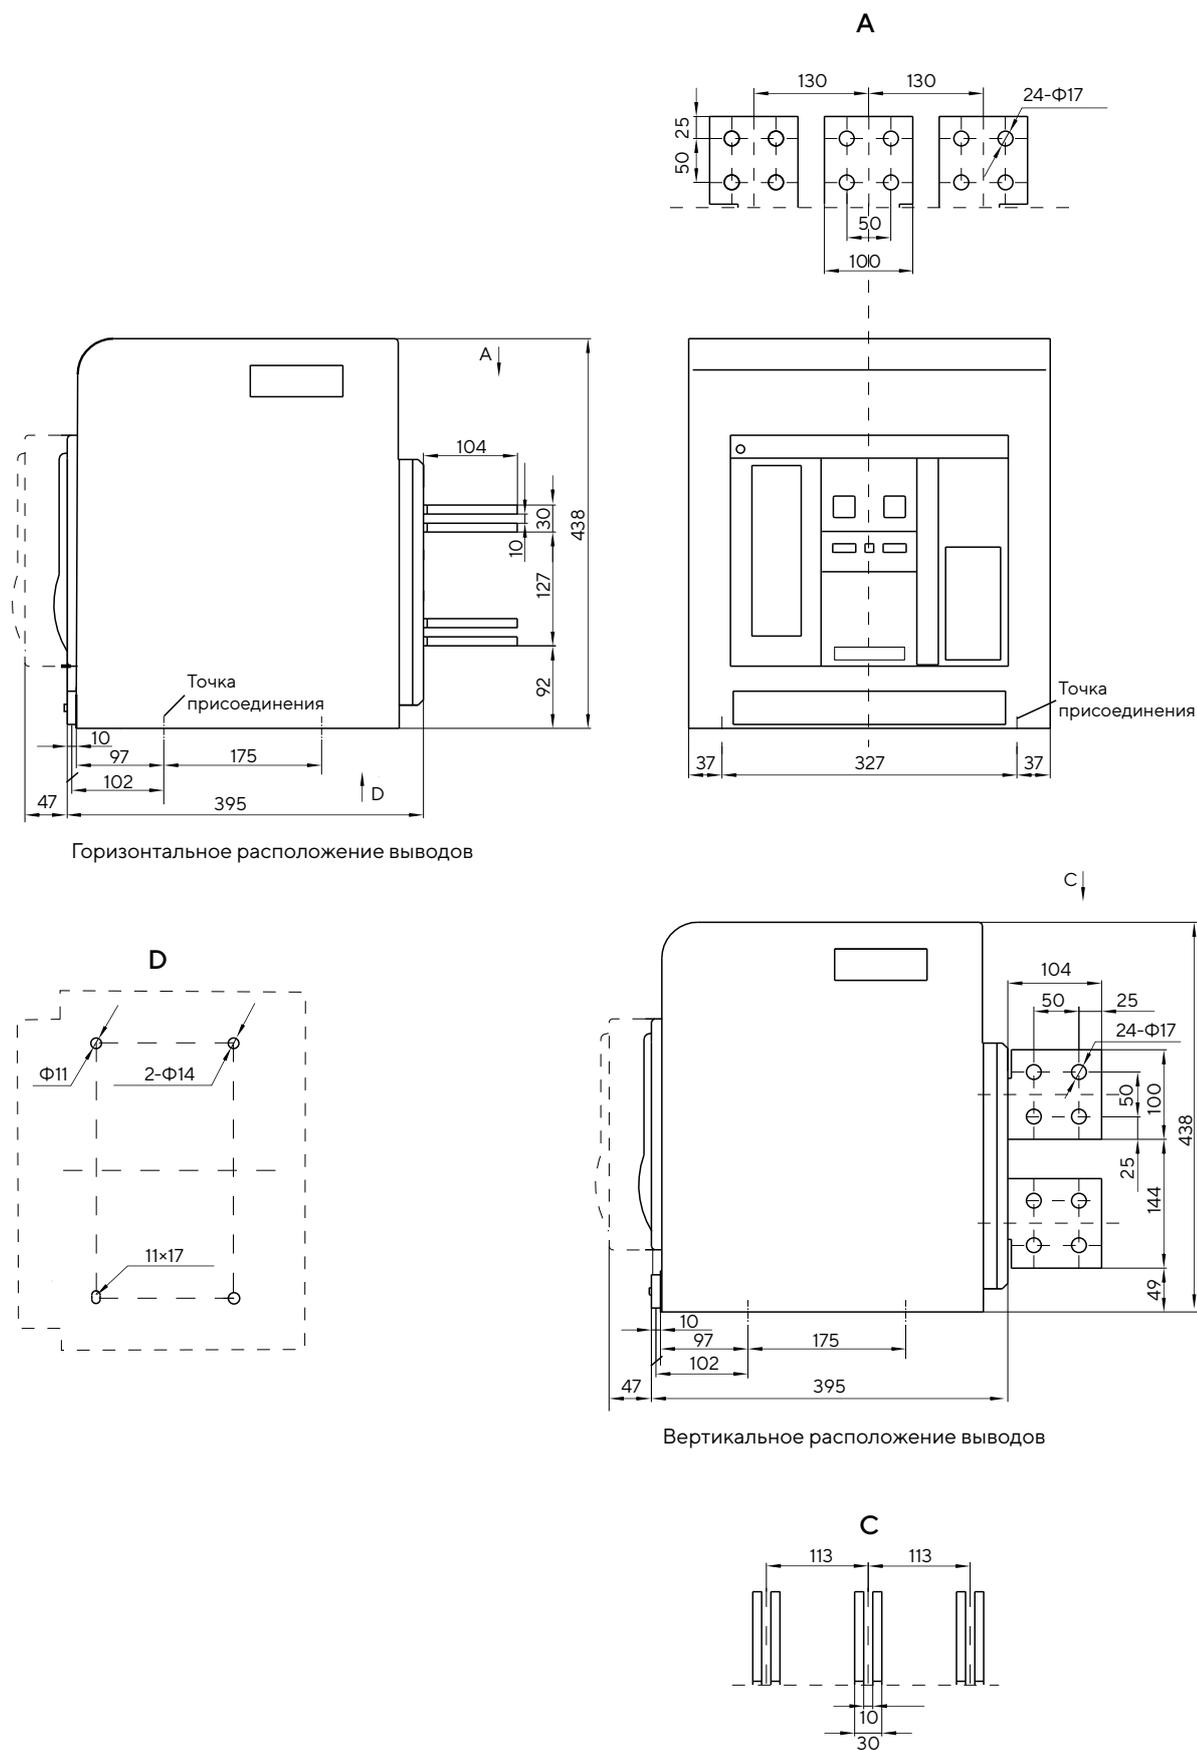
Габаритные размеры выдвижных трехполюсных выключателей типоразмера F (2500~4000 А)
